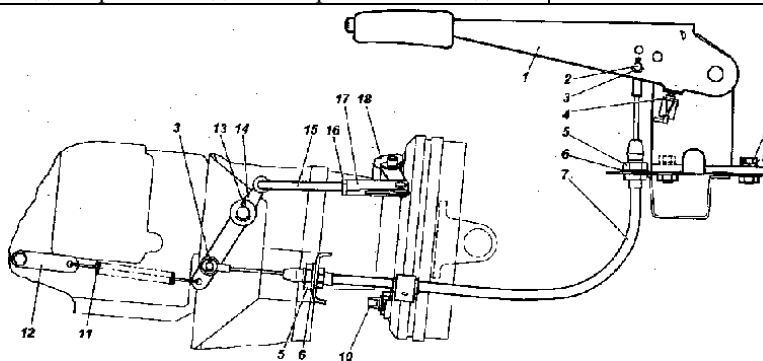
Привод стояночного тормоза: 1 -рычаг привода • сектором; 2 -палец; 3, 13 -шплинт; 4 -выключатель сигнала стояночного тормоза; 5 -гайка; 6 -шайба-7 -трос привода; 8 -болт; 9 -шайба пружинная; 10 -регулирующий винт; 11 -пружина оттяжная; 12 -кронштейн пружины 14 -промежуточный рычаг; 15 -тяга привода; 16 -контргайка; 17 -регулирующая вилка; 18 -рычаг привода
